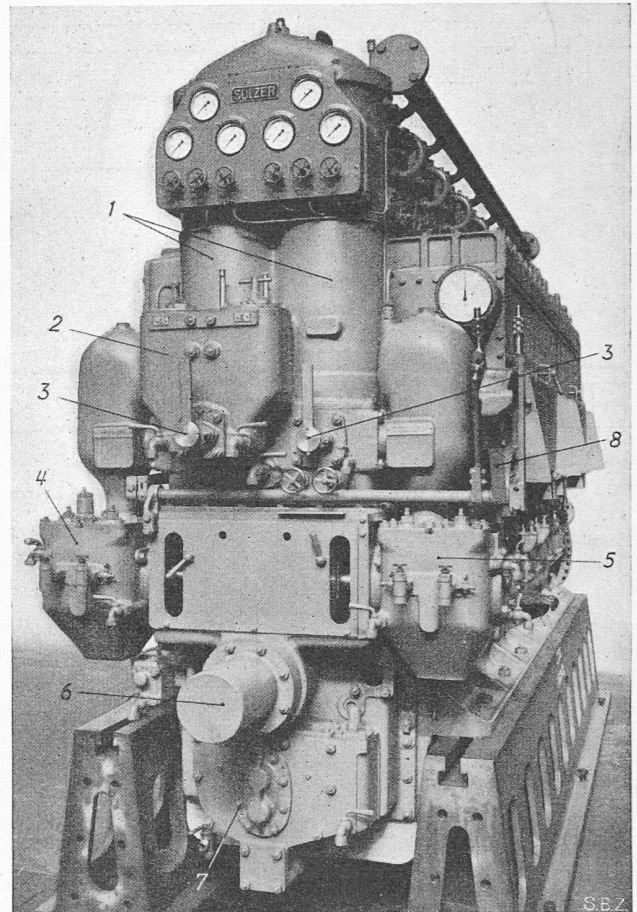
Stirnansicht eines Hauptmotors. 1 Oelkühler, 2 Oelfilter, 3 Umschaltähne zu 1 und 2, 4 Kühlwasserpumpe, 5 Lenzpumpe, 6 Verschaltung zum vorderen Wellenende, 7 Schmier- und Kühlöl-pumpe, 8 Umsteuerung
